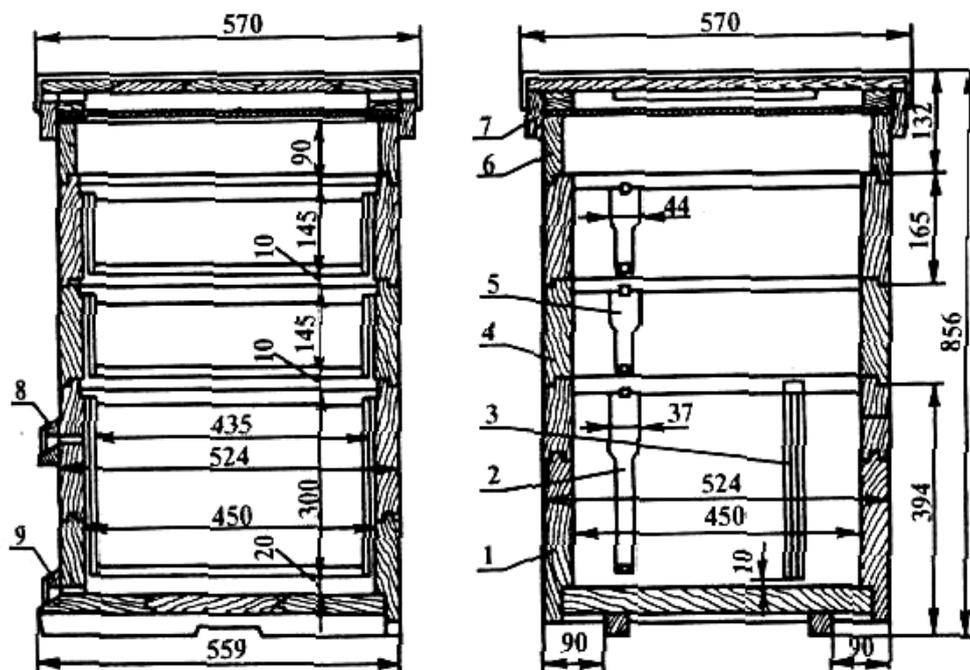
Схема однокорпусного (двенадцатирамочного) улья с двумя магазинными надставками: 1 - корпус; 2 - рамка гнездовая; 3 - диафрагма; 4 - магазин; 5 - рамка магазинная; 6 - подкрышник; 7 - крыша; 8 - задвижка верхнего летка; 9 - задвижка нижнего летка.
